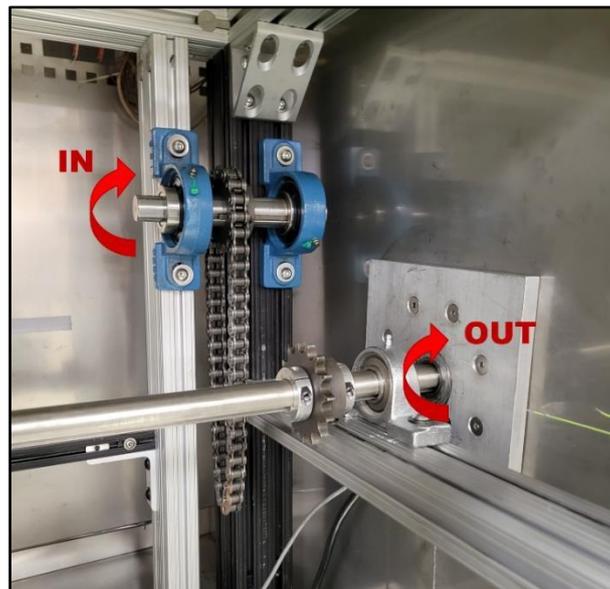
Transmisión de cadena con sprocket momentos antes de ser tensionada
